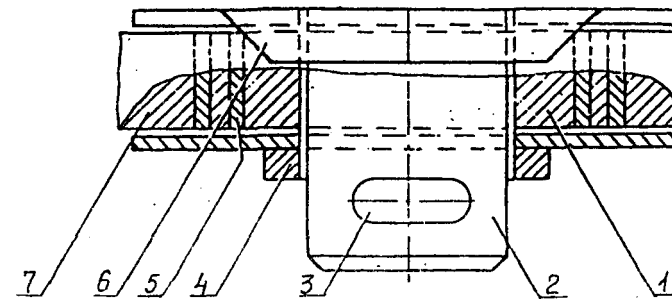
Схема расположения деталей блокирующего устройства в момент входа в зацепление зуба защелки и зуба рычага поворота
